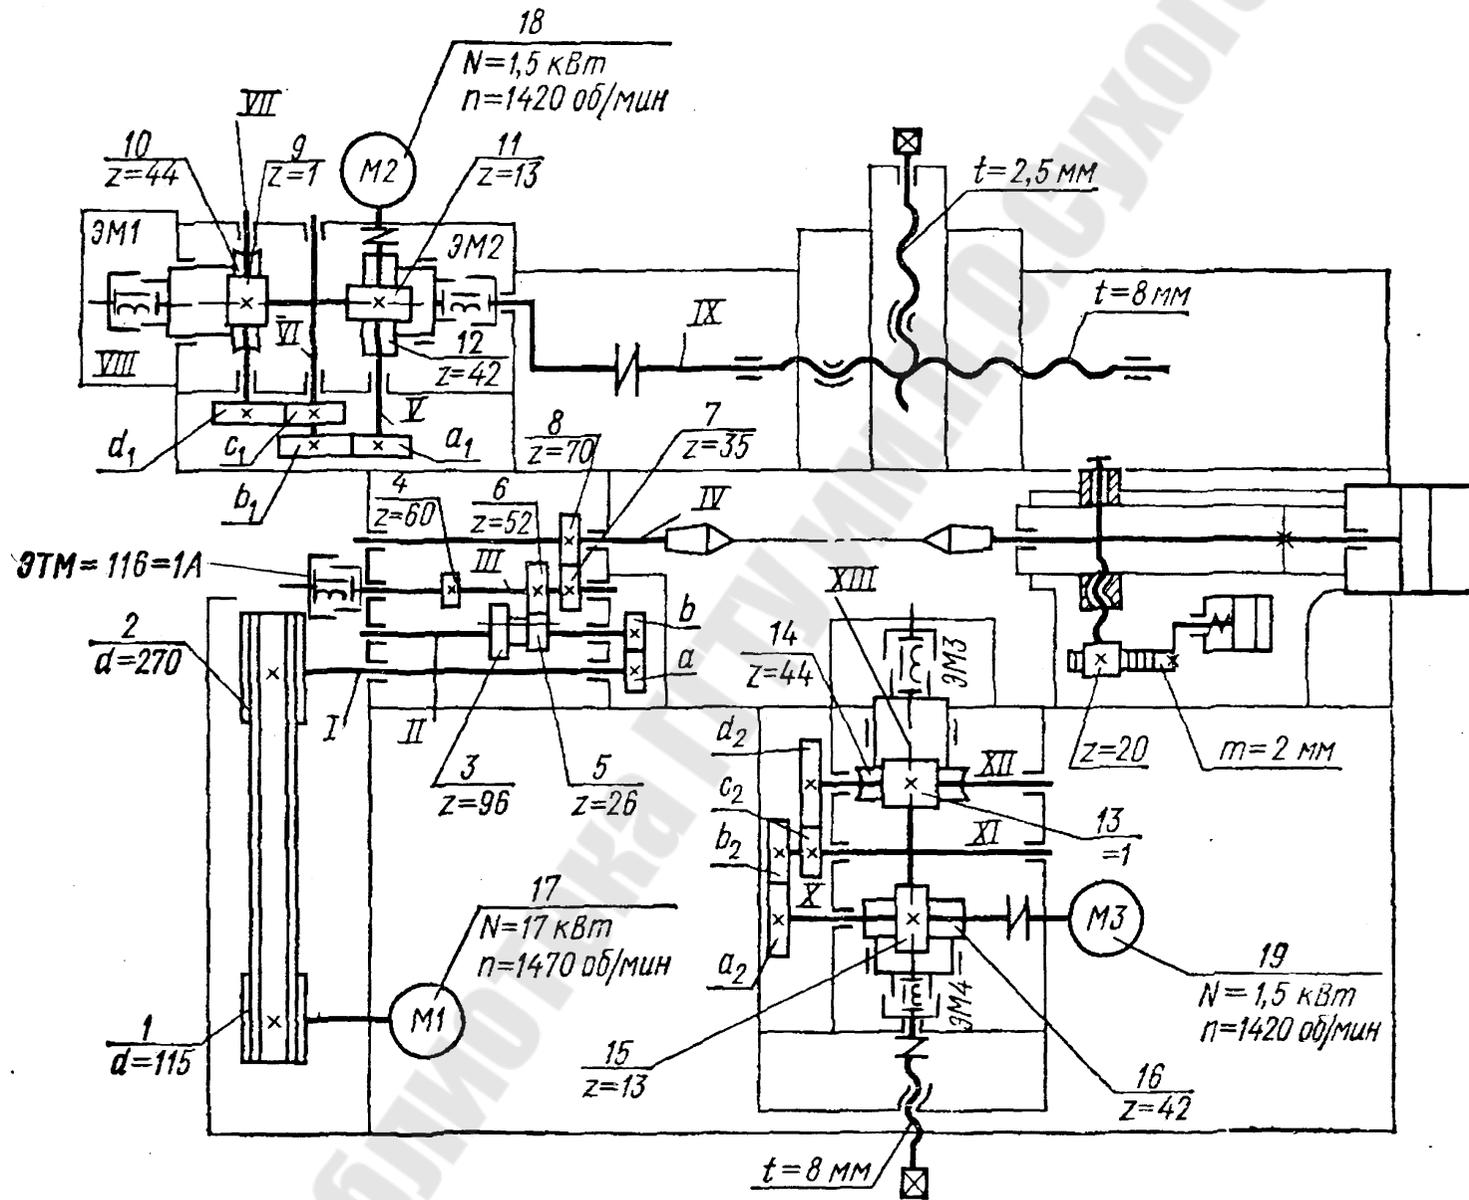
Кинематическая схема токарного многолезцового полуавтомата
